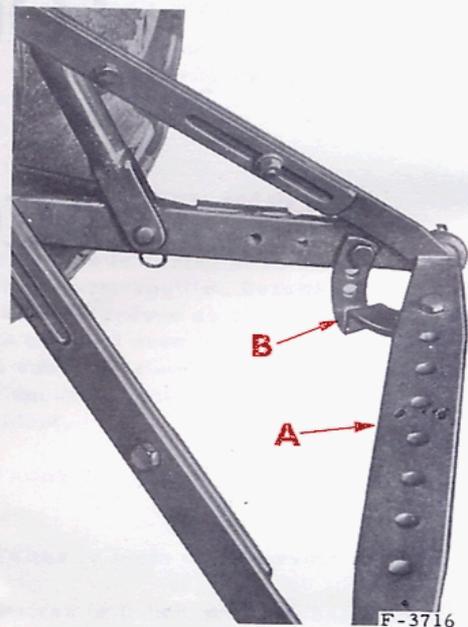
Barre d'attelage pour attelage 3-points. - A. Barre d'attelage. - B. Plaquette de rigidité.
